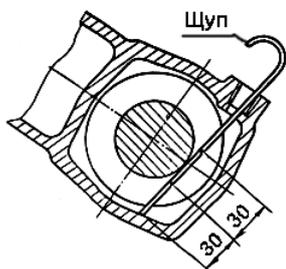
Схема проверки уровня масла в опорных катках (размеры в мм)
